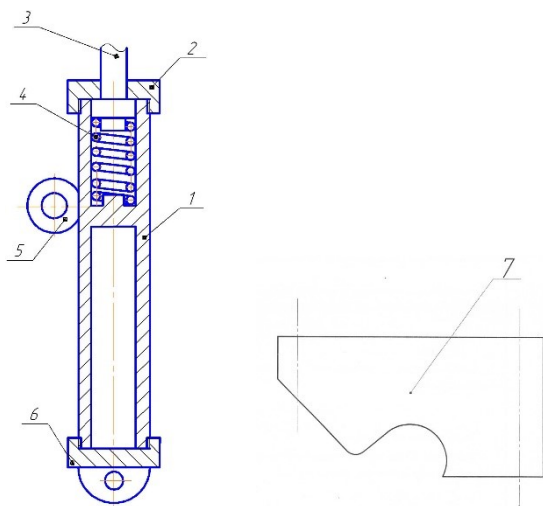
Предохранительный упор для кузова автомобиля – самосвала:
